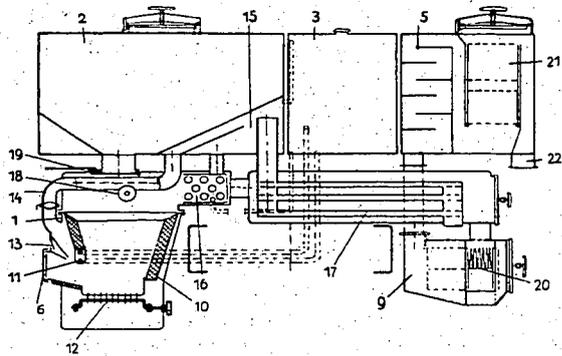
Hansa-Universal-Gaserzeuger mit Zubehör, Schnittbild.
